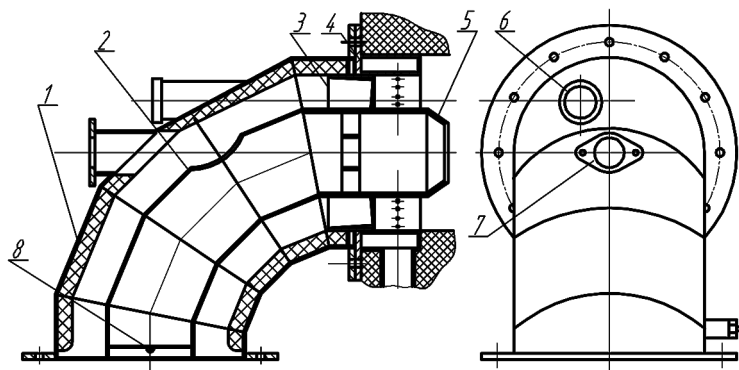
Схема горелочного устройства стадийного сжигания типа ГДС: 1 — корпус; 2 — канал вторичного не закрученного потока воздуха; 3 — лопаточный аппарат; 4 — газовая камера; 5 — коническое сужение канала вторичного воздуха; 6 — окно для визуализации горения; 7 — место для мазутной форсунки; 8 — шибер для регулирования доли вторичного воздуха.
